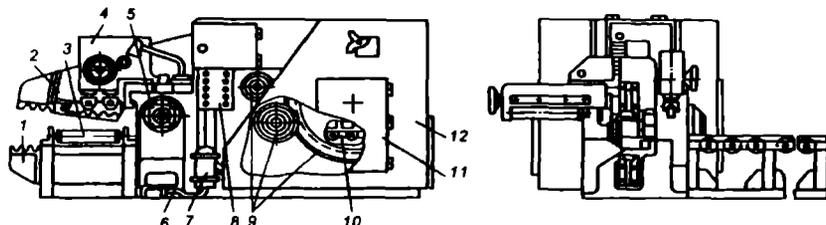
Ножницы Н-2228 аллигаторного типа:
